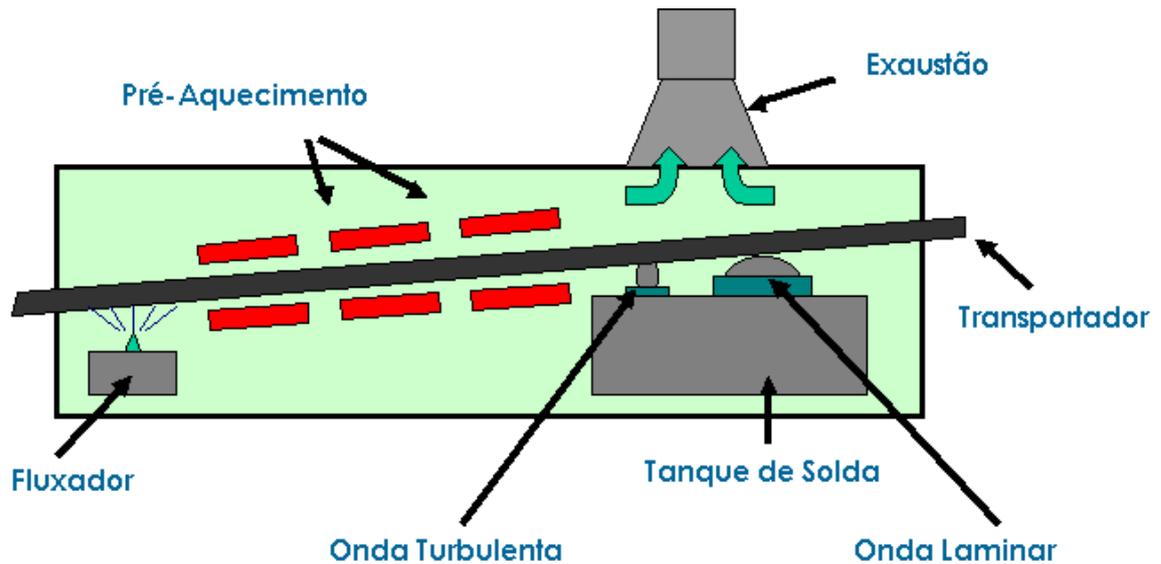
Máquina de Solda em Onda (SMD-ON-LINE)
